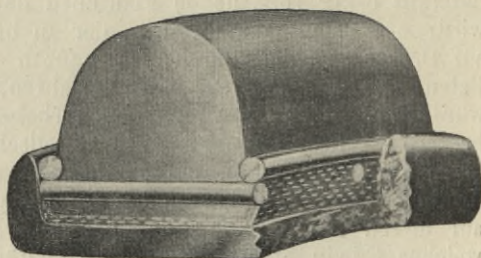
Querschnitt eines Reifens mit seitlichen und quer im Gummi eingebetteten Drähten.
